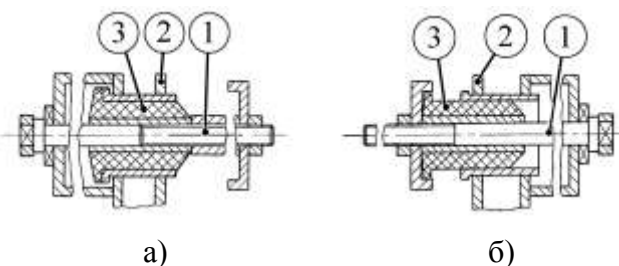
Схема выпрессовки (запрессовки) шарнира рычага задней подвески:
